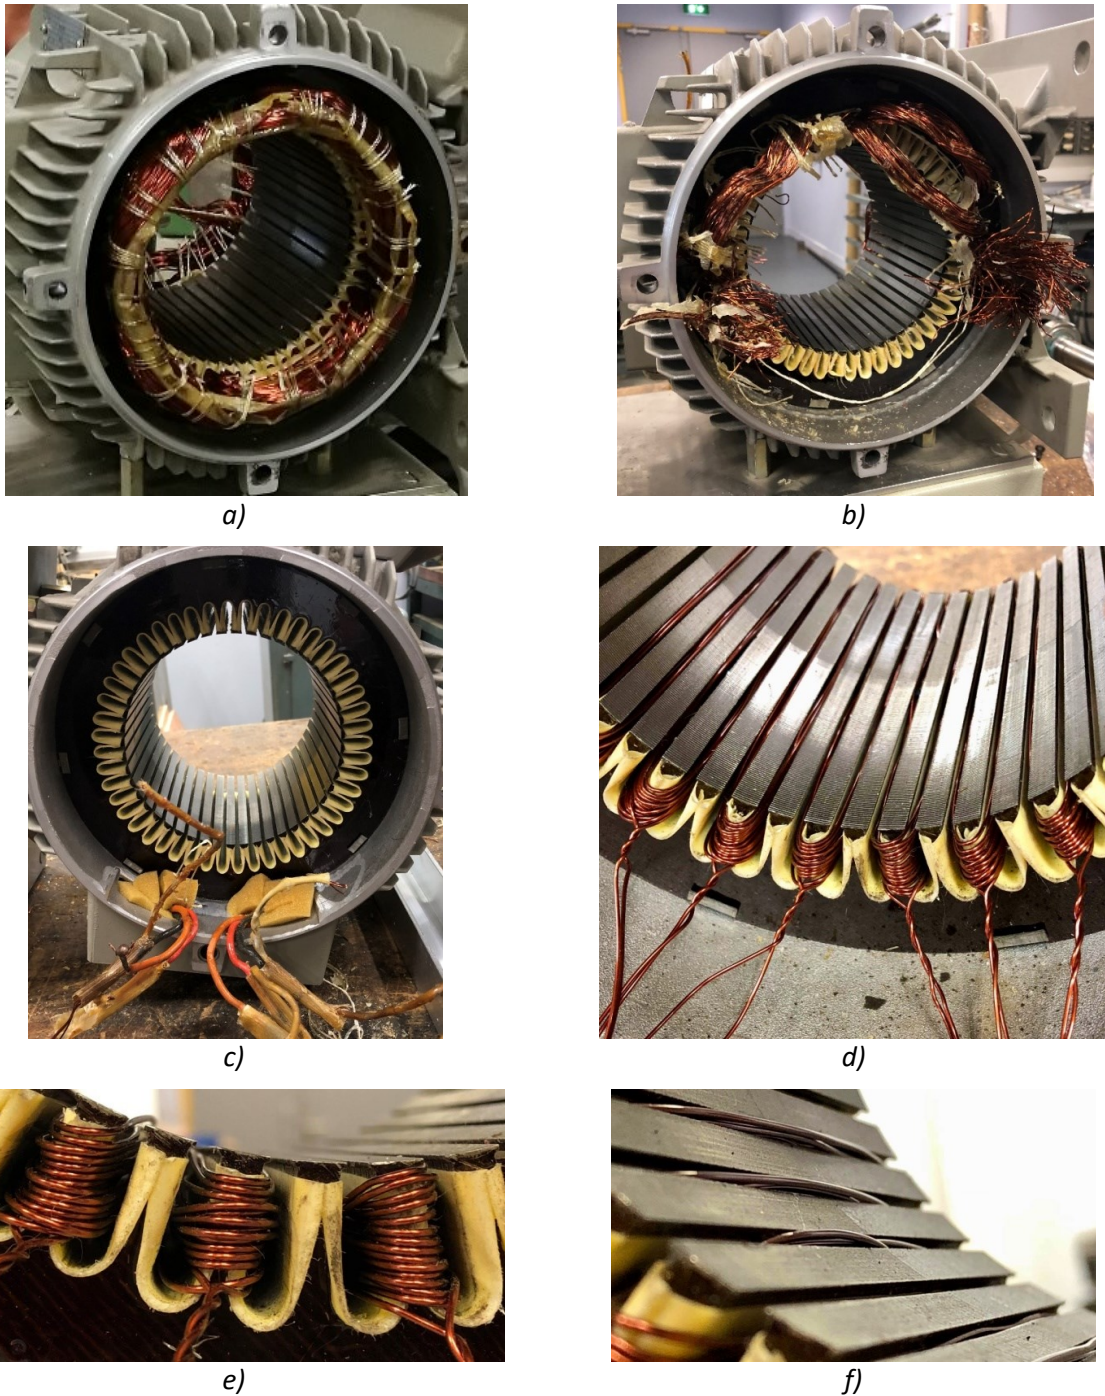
Dé-bobinage et re-bobinage dentaire d'une machine asynchrone à cage de 8 kW : a) bobinage réparti standard ficelé et imprégné, b) démontage du bobinage, c) stator à nu en conservant les isolants dans les encoches, d) bobinage dentaire simple couche, e) une bobine par dent et taux de remplissage faible, e) fils sortant de leur encoche.
